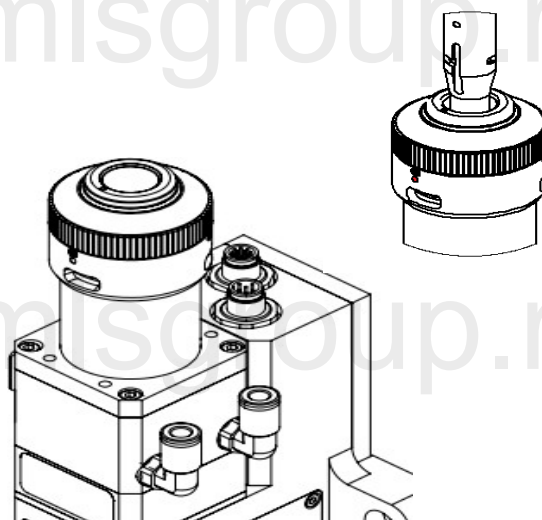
Блок схема подключения источника лазерного излучения с помощью соединителя типа QBN
